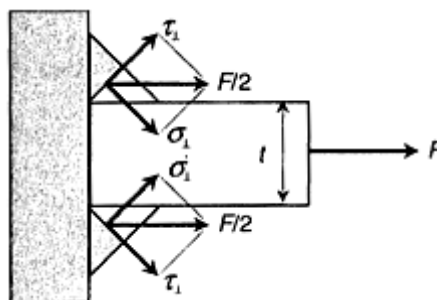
[8.19]. Двойной угловой сварной шов, нагруженный перпендикулярно оси сварки
